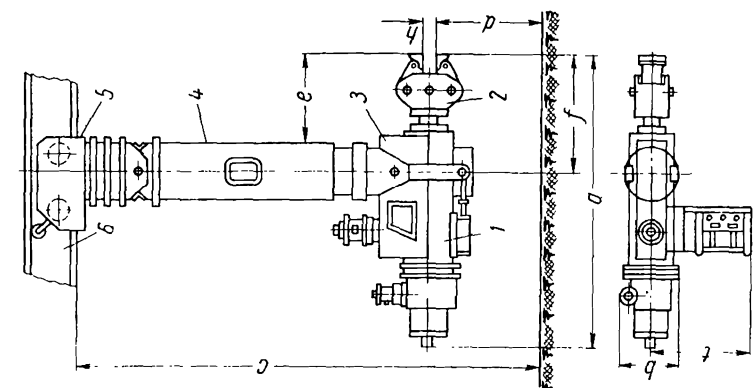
Общий вид подвесного ковочного манипулятора: 1 — корпус манипулятора; 2 — хобот с клещевым зажимом; 3 — кабина управления; 4 — подвешенная колонка; 5 — тележка; 6 — однорельсовый путь
